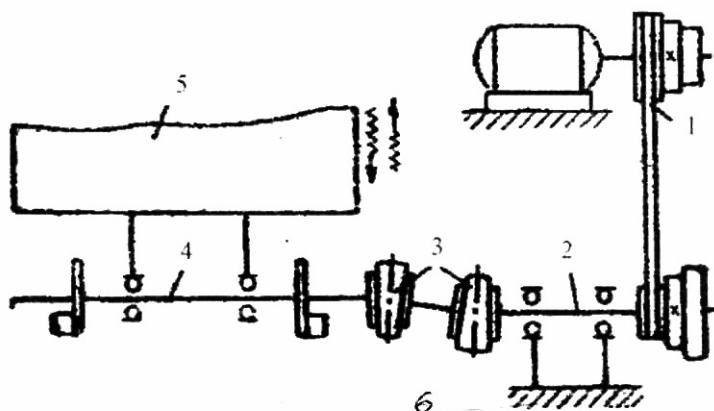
Схема конструкции вибрационного станка с прямоугольной формой рабочей камеры и горизонтальным расположением оси вибратора: 1-электродвигатель (привод) и ступенчатый шкив; 2 - вал промежуточной опоры; 3 - гибкая муфта; 4-вибратор; 5 - рабочая камера; 6-основание
